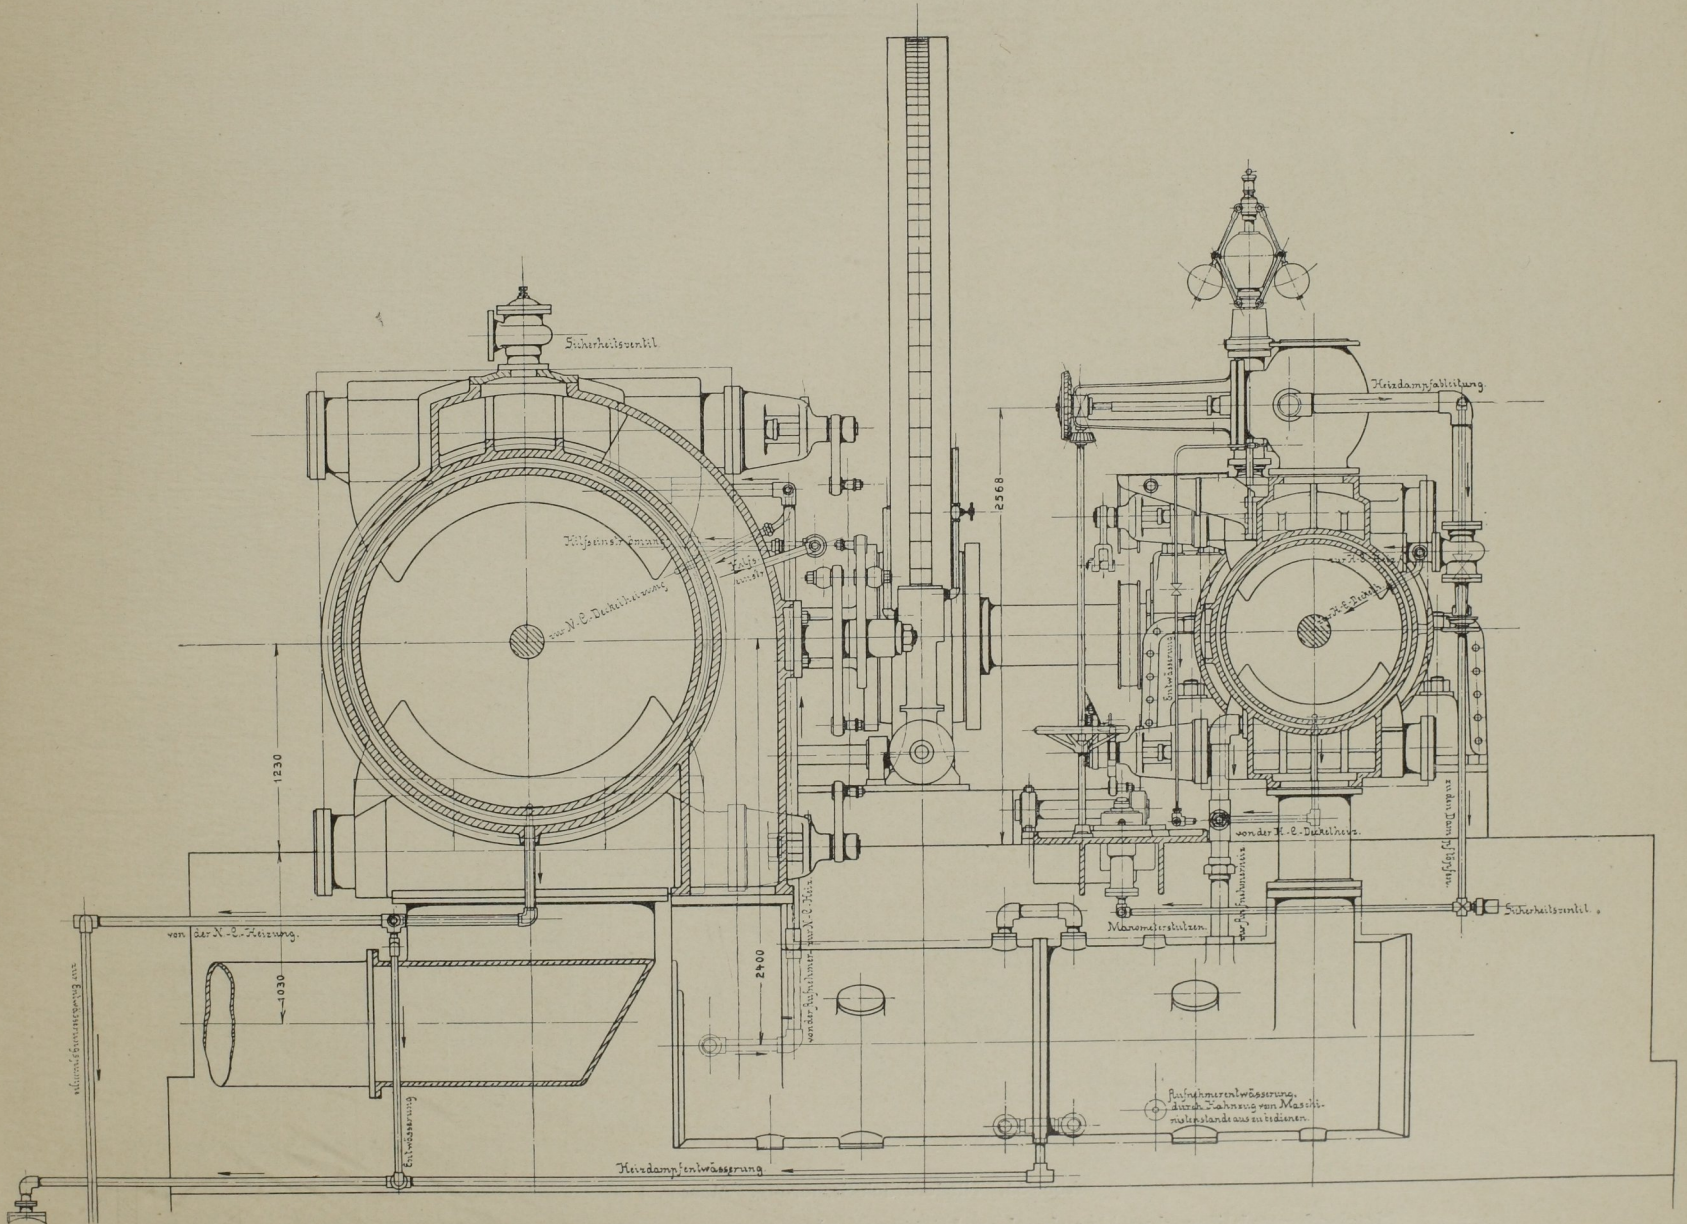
Querschnitt durch die Dampfmaschine. Masst. 1:40.
